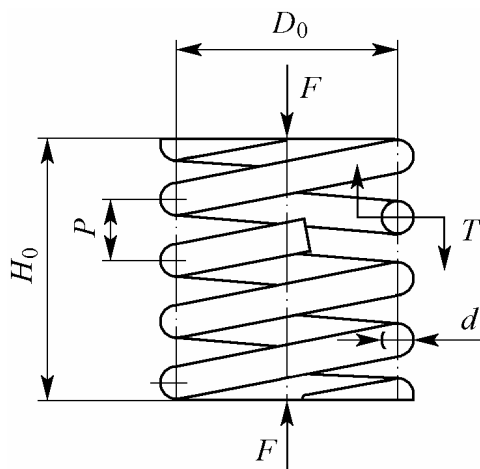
Пружина сжатия с поджатыми и сошлифованными крайними витками
